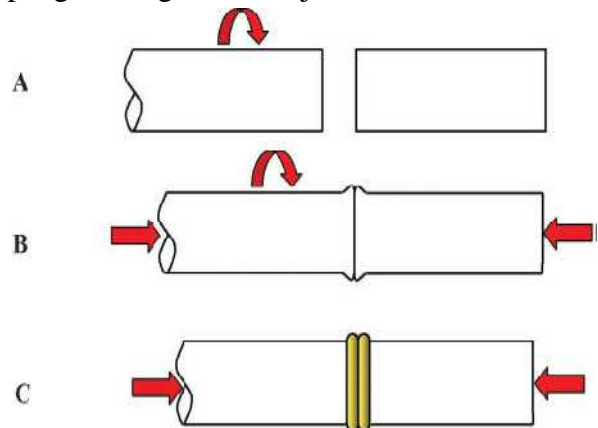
Friction welding (Howes Tom, 2008)
